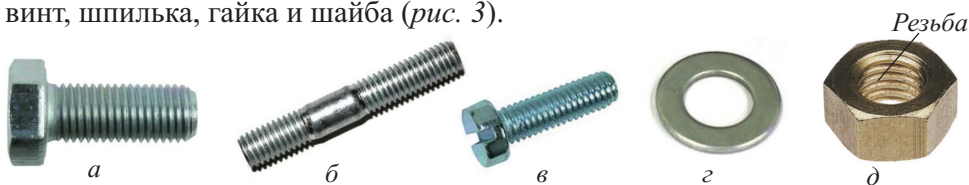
а – болт; б – шпилька; в – винт; г – шайба; д – гайка
